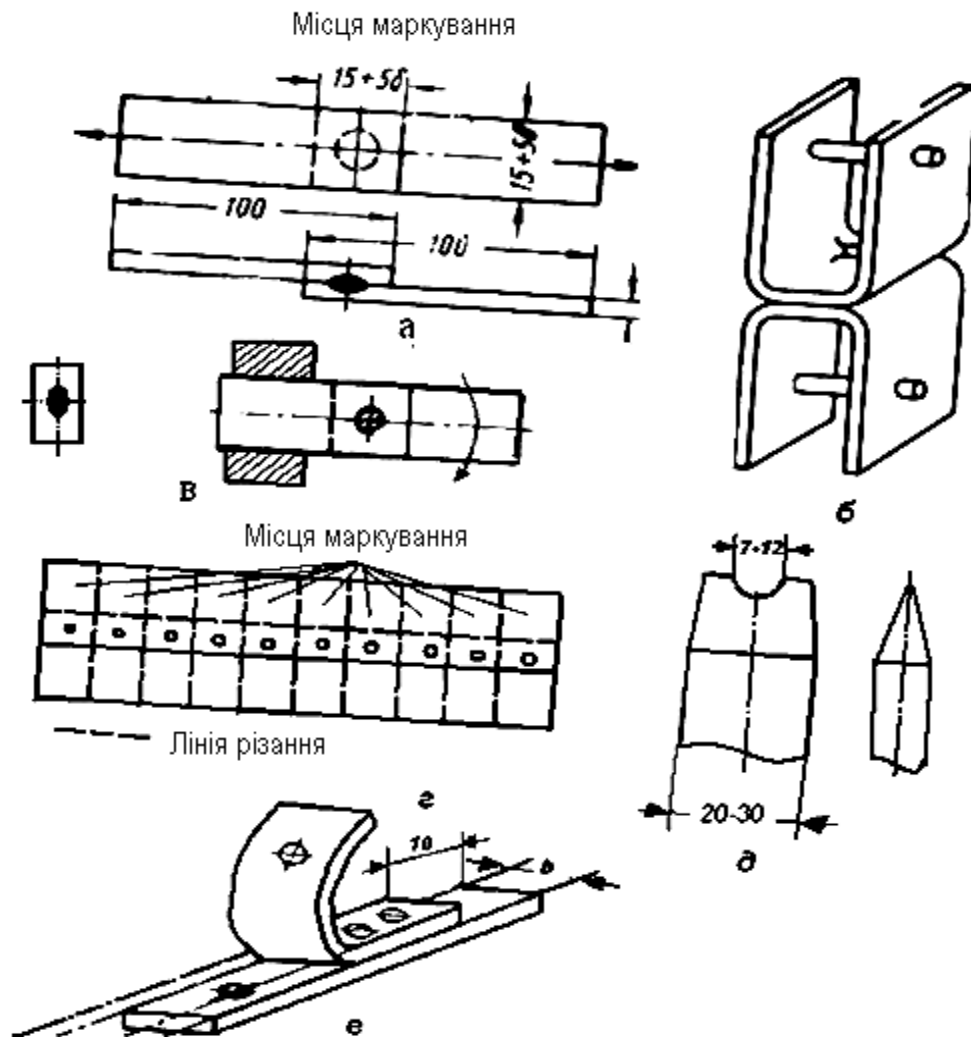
Зразки для випробувань точкового зварювання
